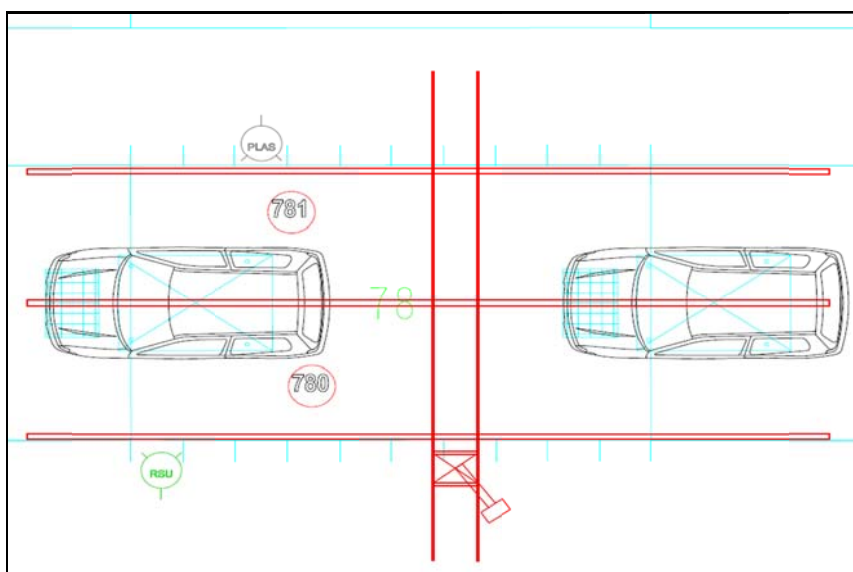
Layout manipulador montaje de butacas (modificación opción 1)
